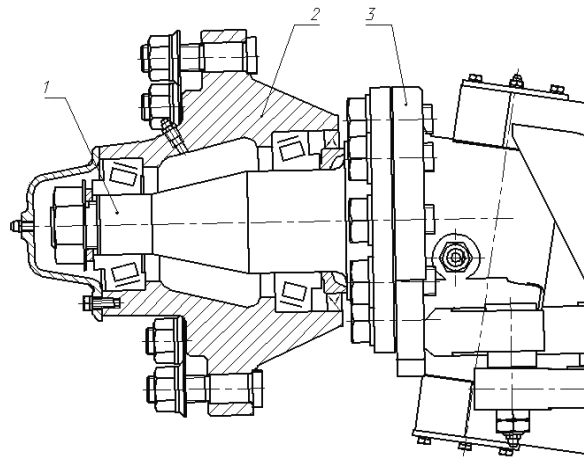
Разъемный поворотный кулак комбайна КЗС-1218: 1 – ось кулака; 2 – ступица; 3 – поворотный кулак
